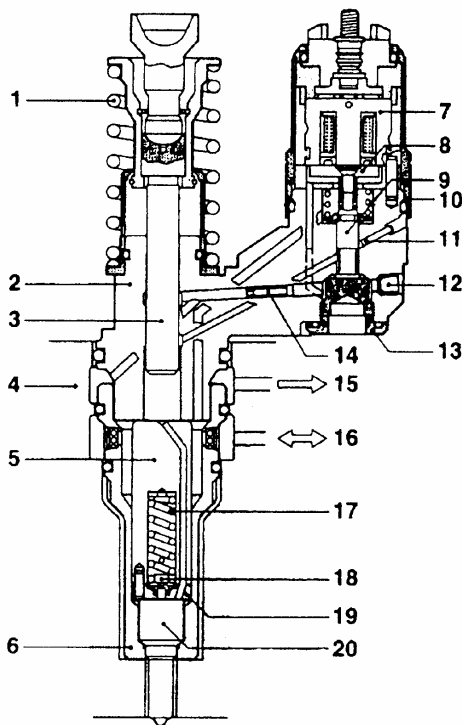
Конструктивна схема насос-форсунки фірми Bosch [6]:
